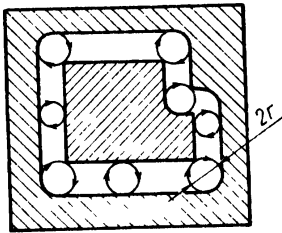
Обробка отвору інструментом, що виконує планетарний рух
